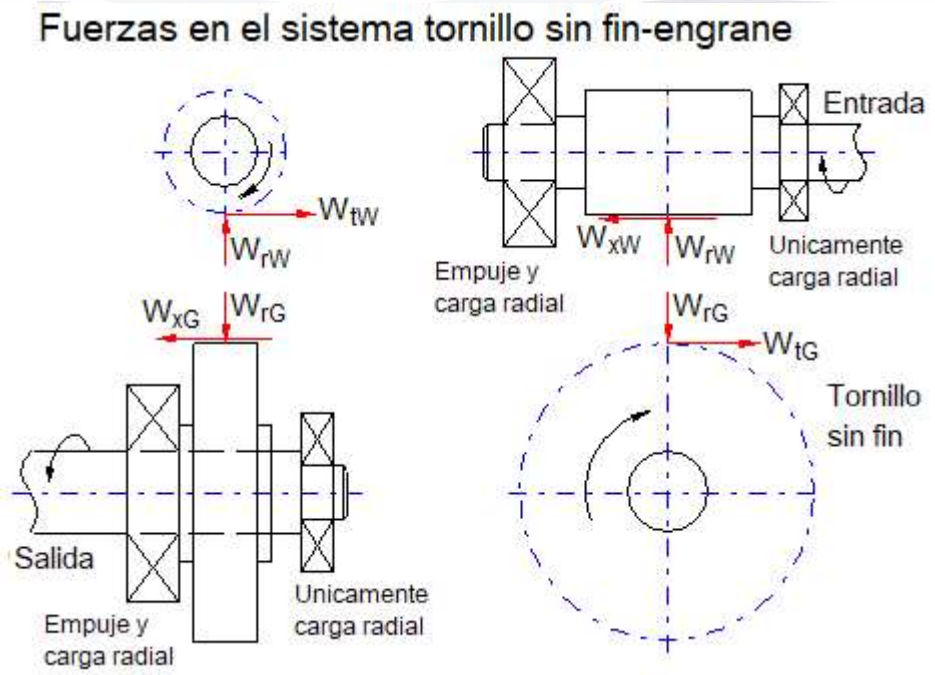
, Fuerzas en el sistema tornillo sin fin - engranaje.
